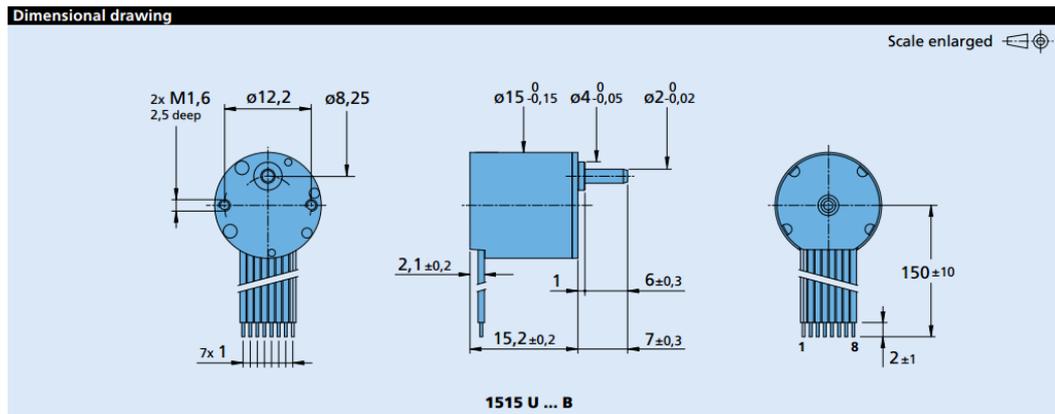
Dimensiones del motor y reductora del crawler obtenida de Faulhaber
